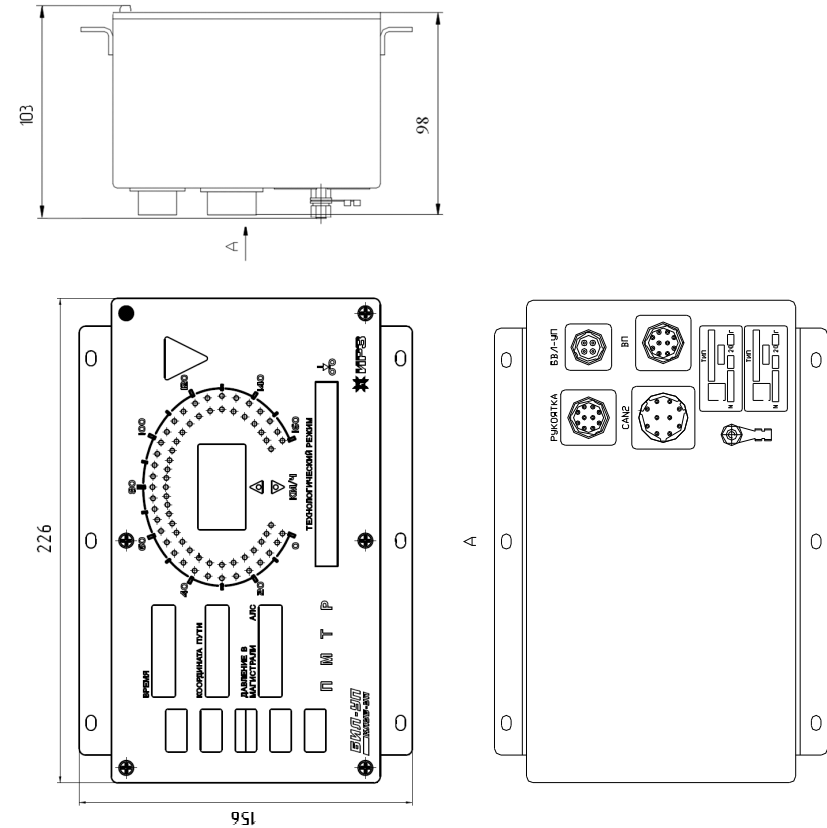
Внешний вид и габаритные размеры блока БИЛ-УП-01 36993-310-00-01
